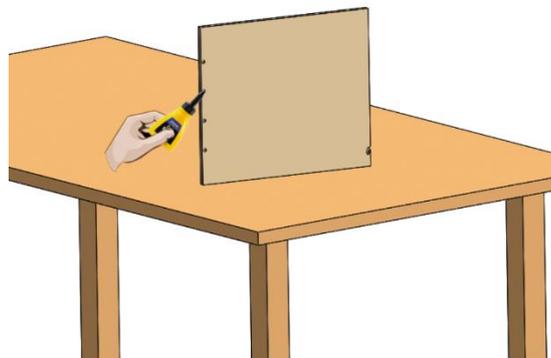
Paso 3 del ensamblaje del cajón (conjunto 2)
